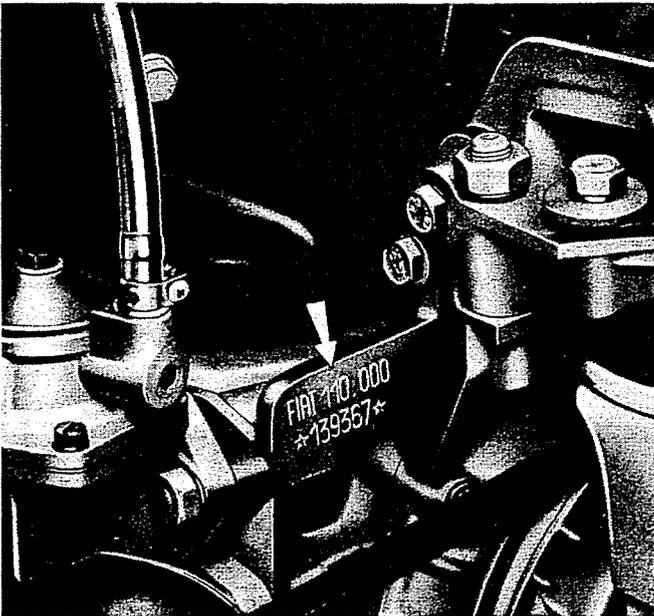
Kennnummer des Motors, am Kurbelgehäuse eingepreßt.
